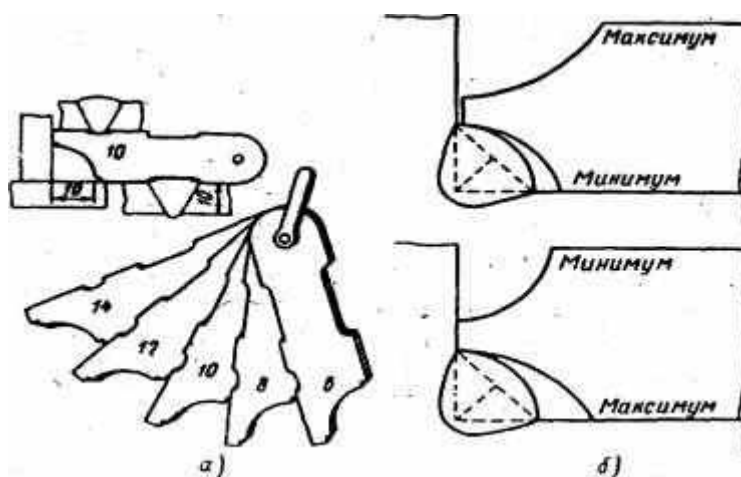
Шаблоны для контроля размеров сварных швов: а – набор шаблонов для контроля угловых и стыковых швов; б – шаблон для проверки размеров угловых швов
